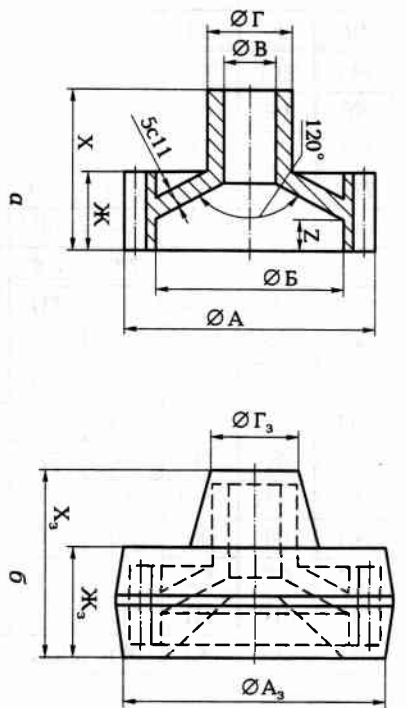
Эскиз обрабатываемого цилиндрического зубчатого колеса с прямыми зубьями:
